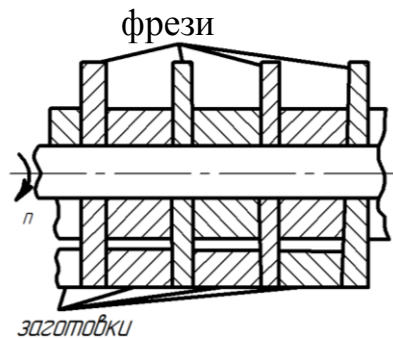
Розрізування прокату декількома фрезами на горизонтально – фрезерному верстаті
